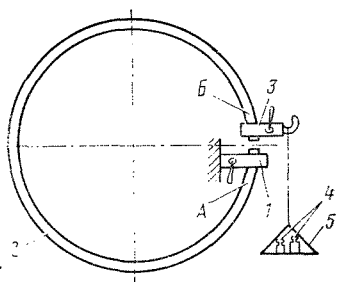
Схема проверки упругости пружины уплотнительного кольца
